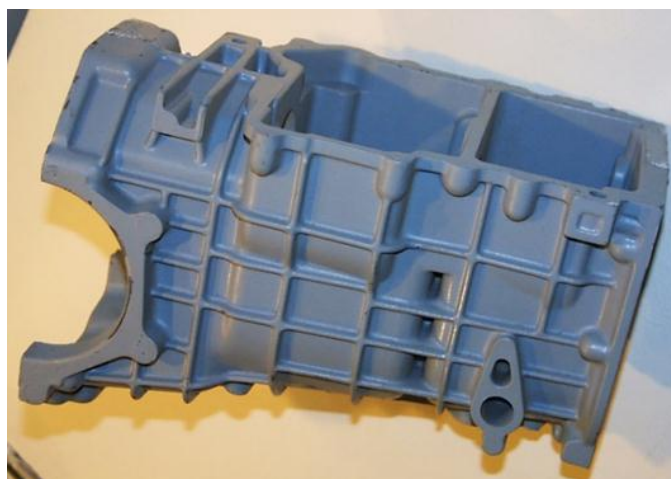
Корпус редуктора из магниевого сплава МЛ15
